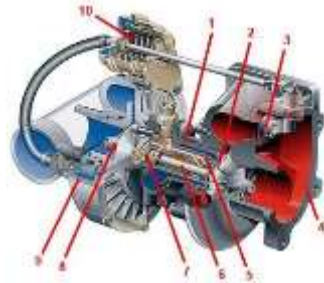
Турбокомпресор: 1 – корпус підшипників; 2 – турбінне колесо; 3 – перепускний клапан; 4 – корпус турбіни; 5 – мастильні канали; 6 – вал ротора; 8 – компресорне колесо; 10 – пневмопривод перепускного клапана
